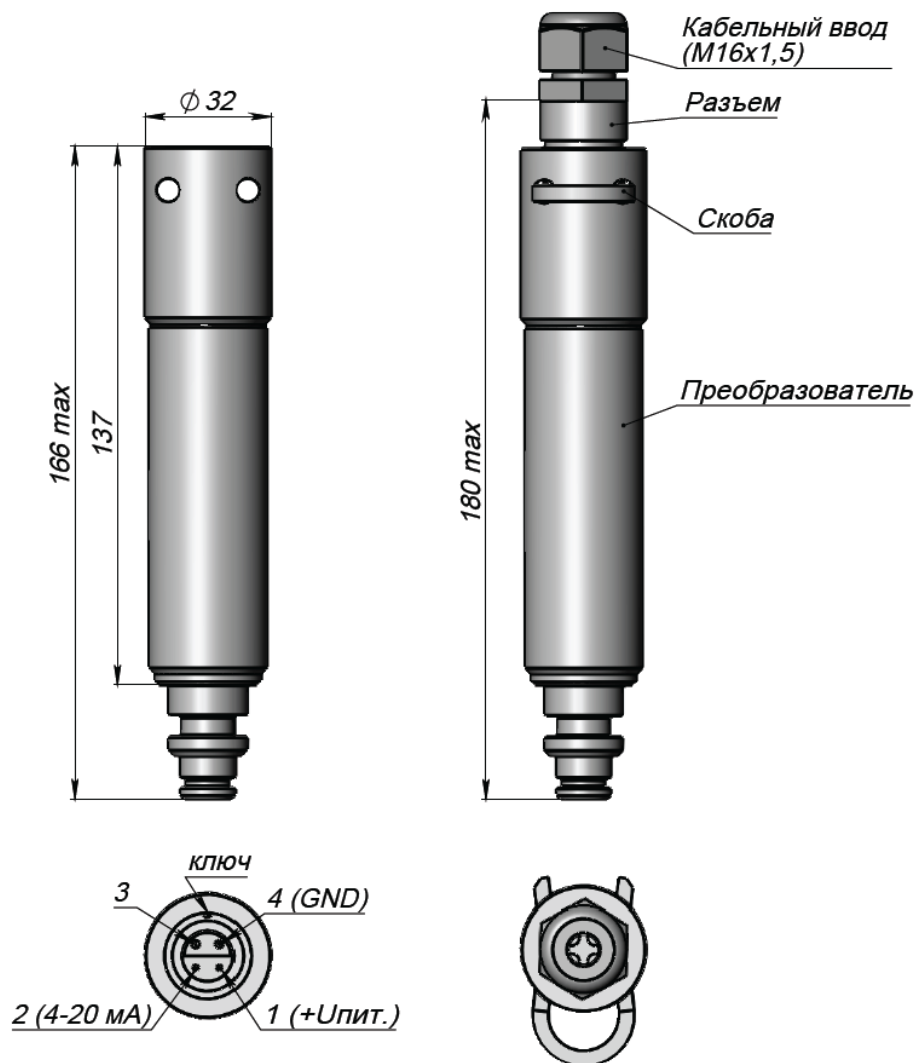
Внешний вид и габаритные размеры преобразователей PR-28/Exd
